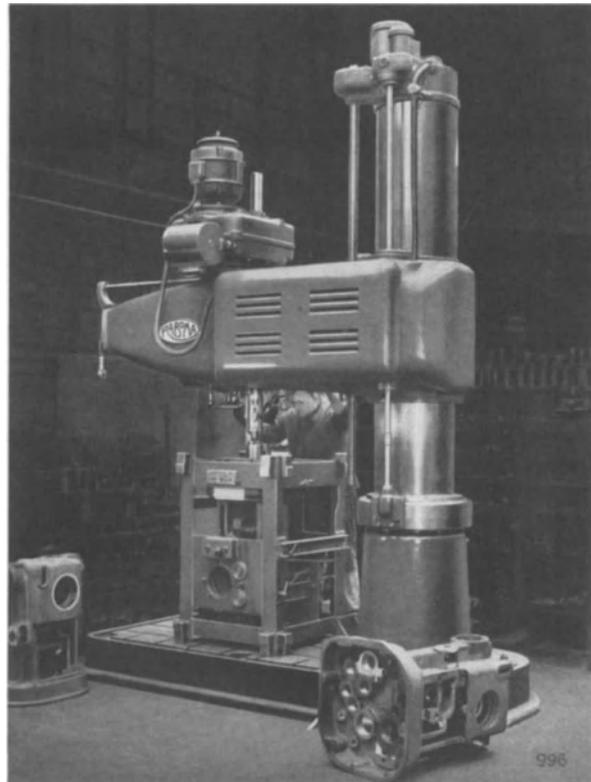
Große geschweißte Bohrvorrichtung
